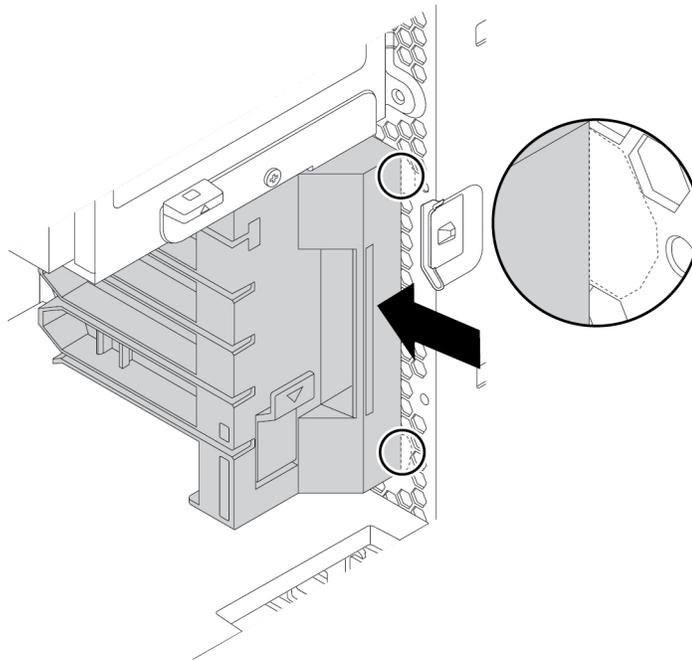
Asegurarse de que el conjunto del ventilador frontal esté bien instalado
